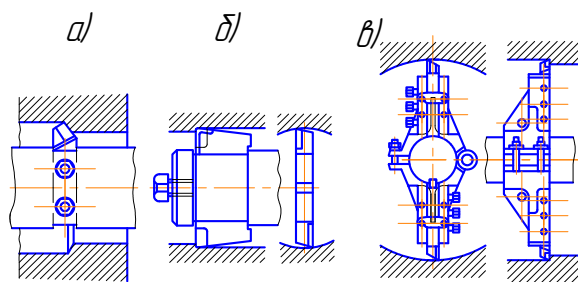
Обработка основных отверстий: а – однорезцовый блок; б – двурезцовый блок; в – регулируемый блок.
